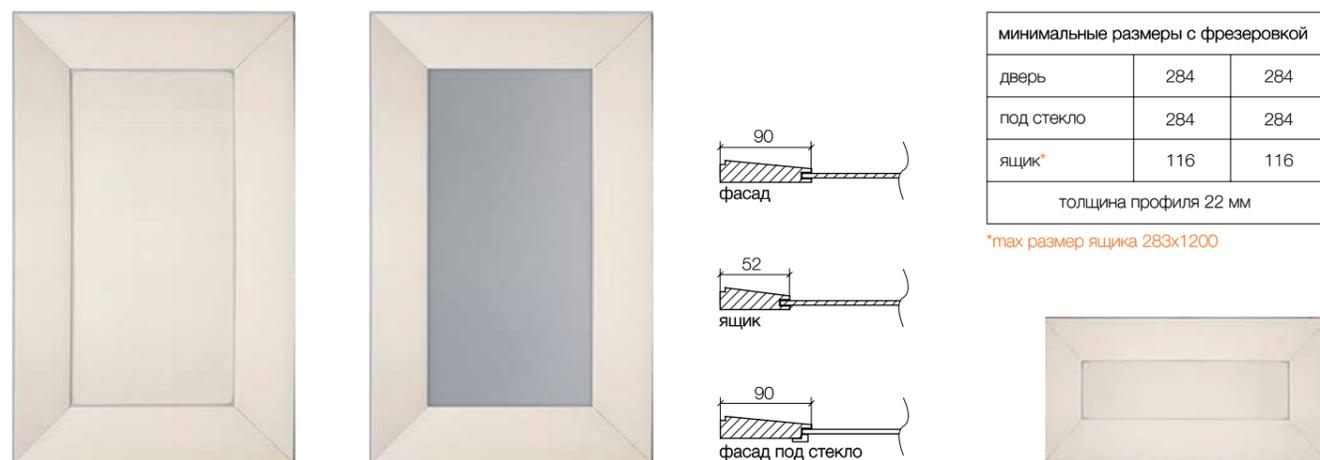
Максимальный размер сборного фасада 1600x1300, минимальный размер 116x116
